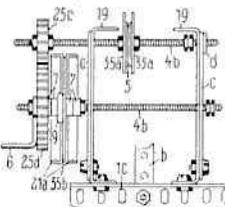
Seitenansicht mit Ansicht der Bohrspindel.
